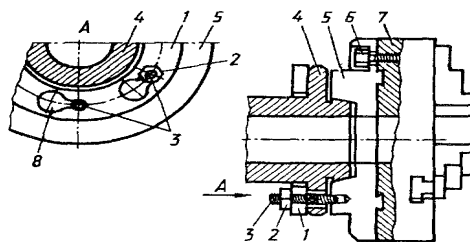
Закріплення токарного патрона з посадкою на конус: 1- шайба; 2 - гайка; 3 - нарізна шпилька, 4 - шпindelъ; 5 - планшайба; 6 – гвинт; 7– корпус патрона; 8 - вікно проріз) шайби для проходження гайки під час заміни патрона (гайку умовно не показано)
